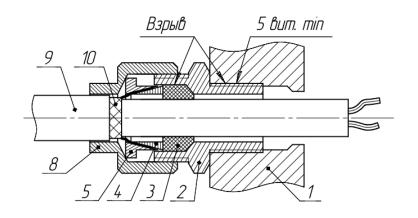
Конструкция оповещателя светового Орбита МК С Н (корпус из коррозионно-стойкой стали).
